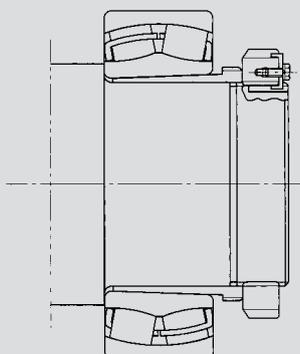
Цилиндрический вал, стопорный бугель (стяжная втулка)
